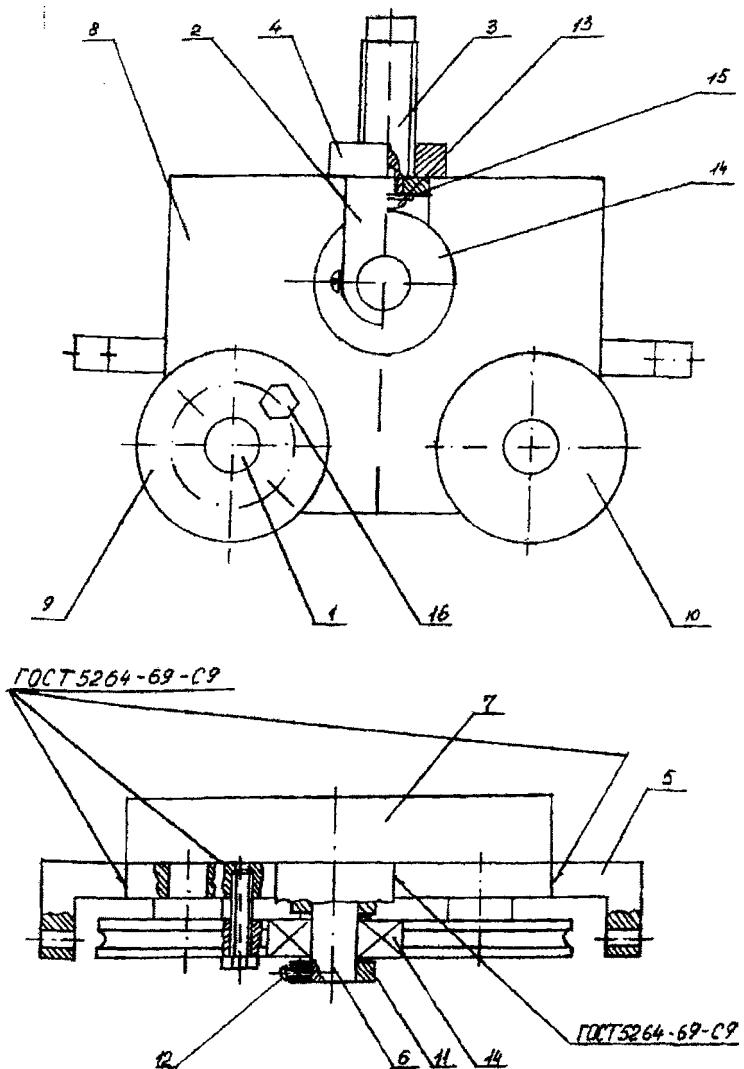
Устройство для намотки проволоки: 1 – ось ролика; 2 – вилка; 3 – винт; 4 – кронштейн; 5 – направляющая; 6 – ось подшипника; 7 – планка; 8 – плита; 9 – ролик специальный; 10 – ролик; 11 – шайба; 12 – винт; 13 – фиксатор; 14 – подшипник; 15 – шайба; 16 – болт
